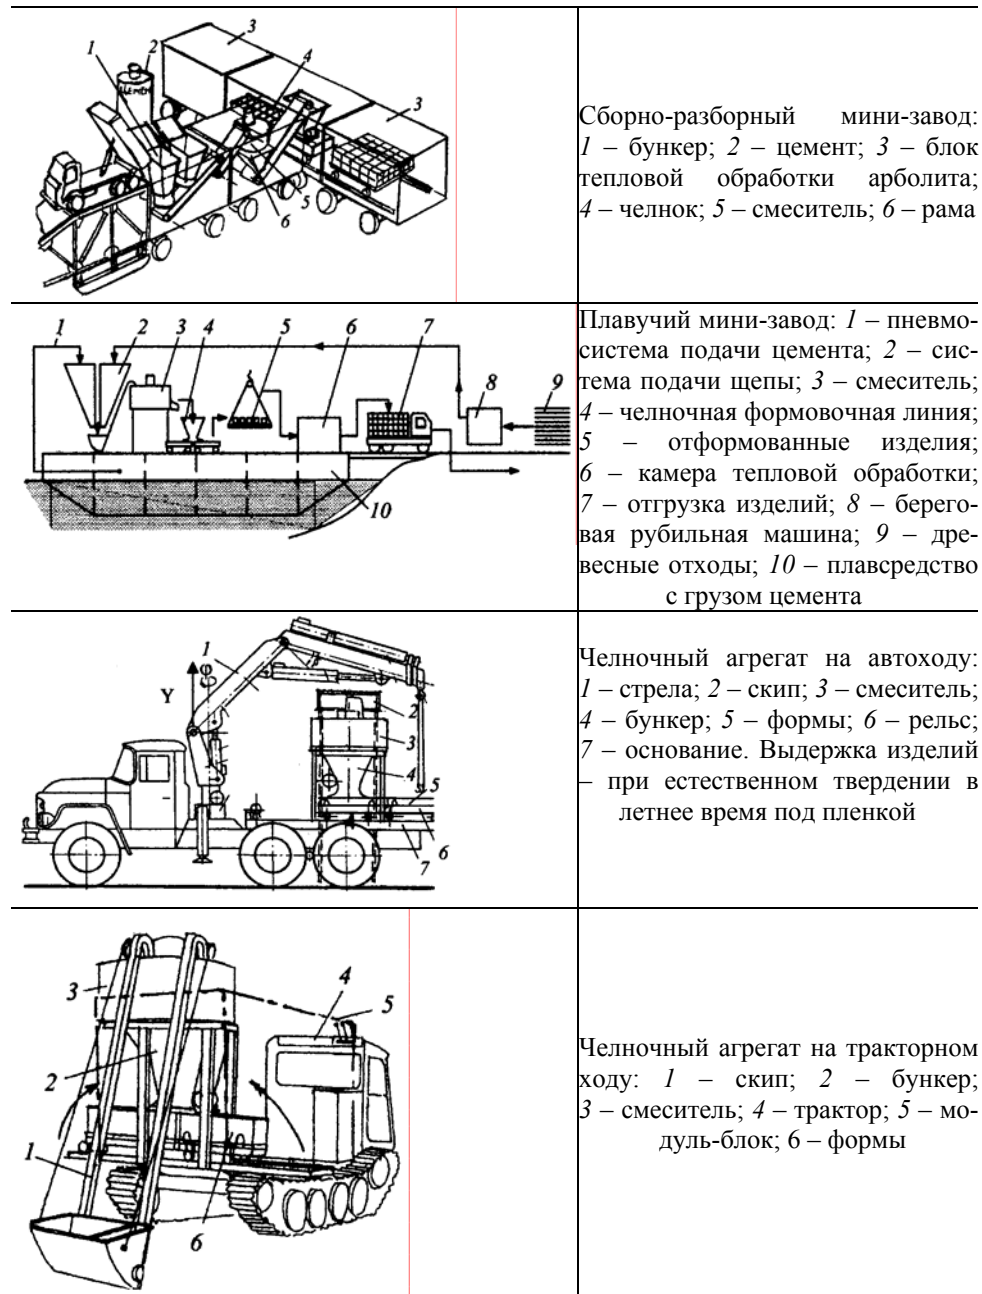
Схема базирования челночного смесительно-формовочного агрегата
